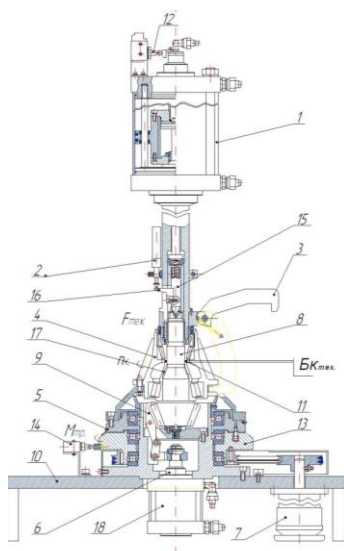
Стенд для регулировки преднатяга подшипников ведущей шестерни редуктора ( 1-силовой привод, 2- индуктивный датчик, 3 – рычаг для захвата корпуса, 4- корпус подшипникового узла, 5 – ведомый диск торсионного устройства для контроля момента трения, 6 – силовой привод для закрепления ведущей вал-шестерни, 7 - электродвигатель-редуктор, 8- вал-шестерня, 9 – рычаг-прихват для закрепления ведущей шестерни, 10 – стол стенда, 11-подшипник верхний, 12 – концевой выключатель, 13 – ведущий диск торсионного устройства для контроля момента трения, 14 – датчик контроля момента трения, 15 – плавающий центр, 16 – рычаг-коромысло измерительного датчика, 17 – дистанционная распорная втулка, 18 – пневмопривод механизма закрепления шестерни)
